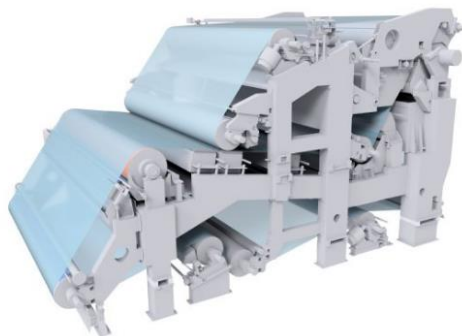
Двосітковий пристрій для формування DuoFormer Base II
